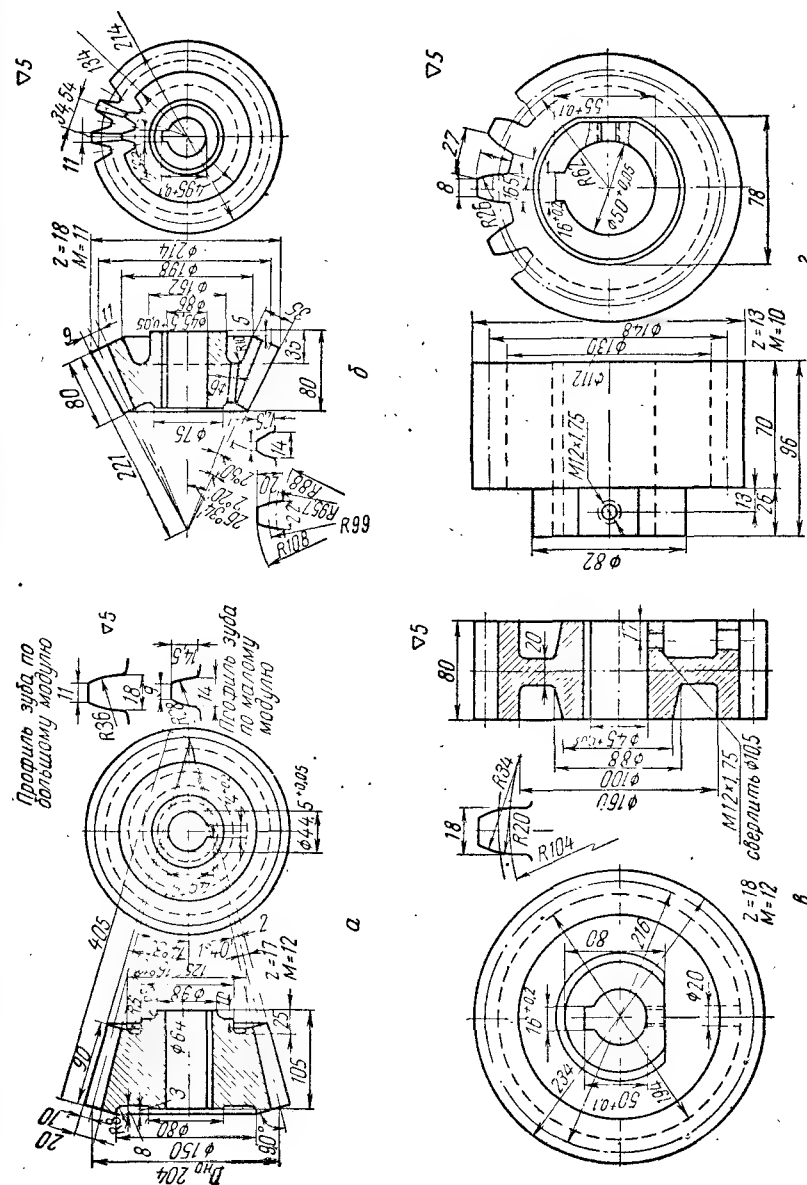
Малые шестерни ветродвигателей ТВ-8 и ТВМ-8:
